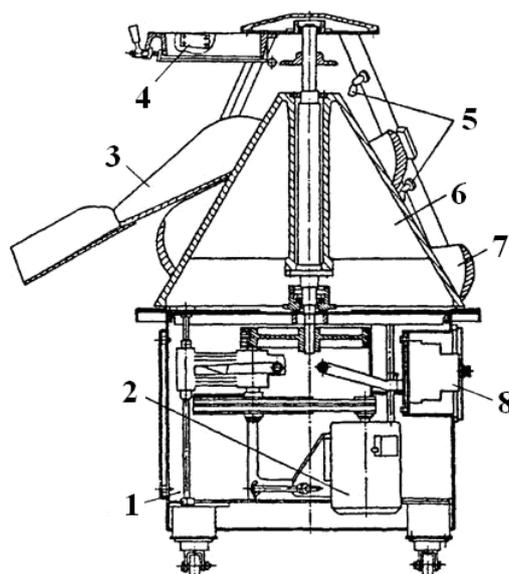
Тестоокруглитель А2-ХПО-6 с конической несущей поверхностью и наружным формующим органом
